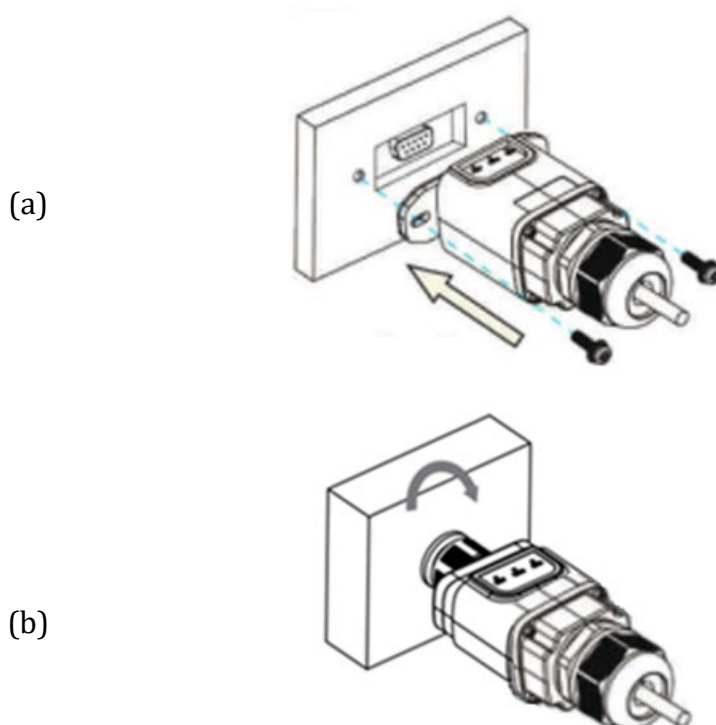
Inserimento e fissaggio dell'adattatore ethernet
